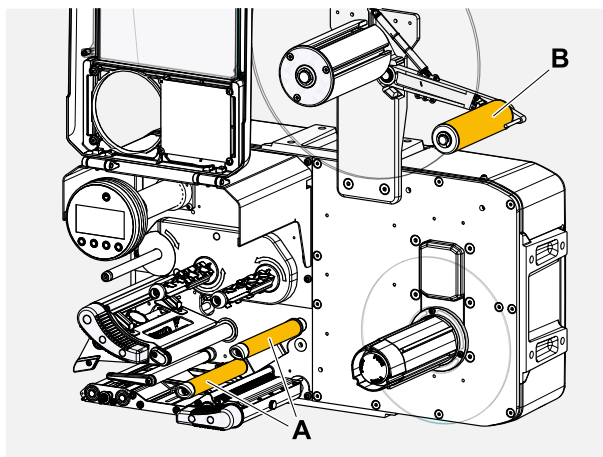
Ejes y rodillos de inversión en el XPA 93x.
